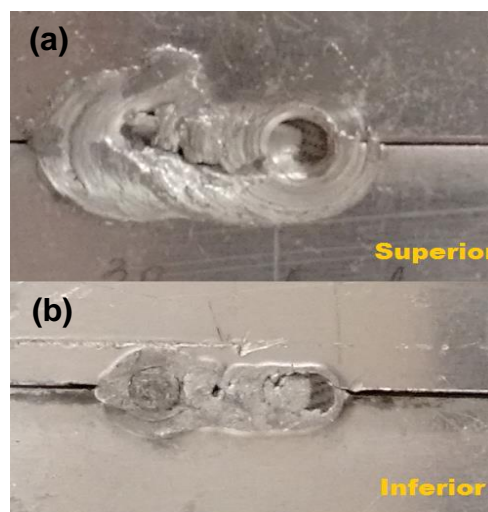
Ensaio para a determinação da altura do pino da ferramenta com um pino de 3 mm. Vistas (a) superior e (b) inferior da solda.
